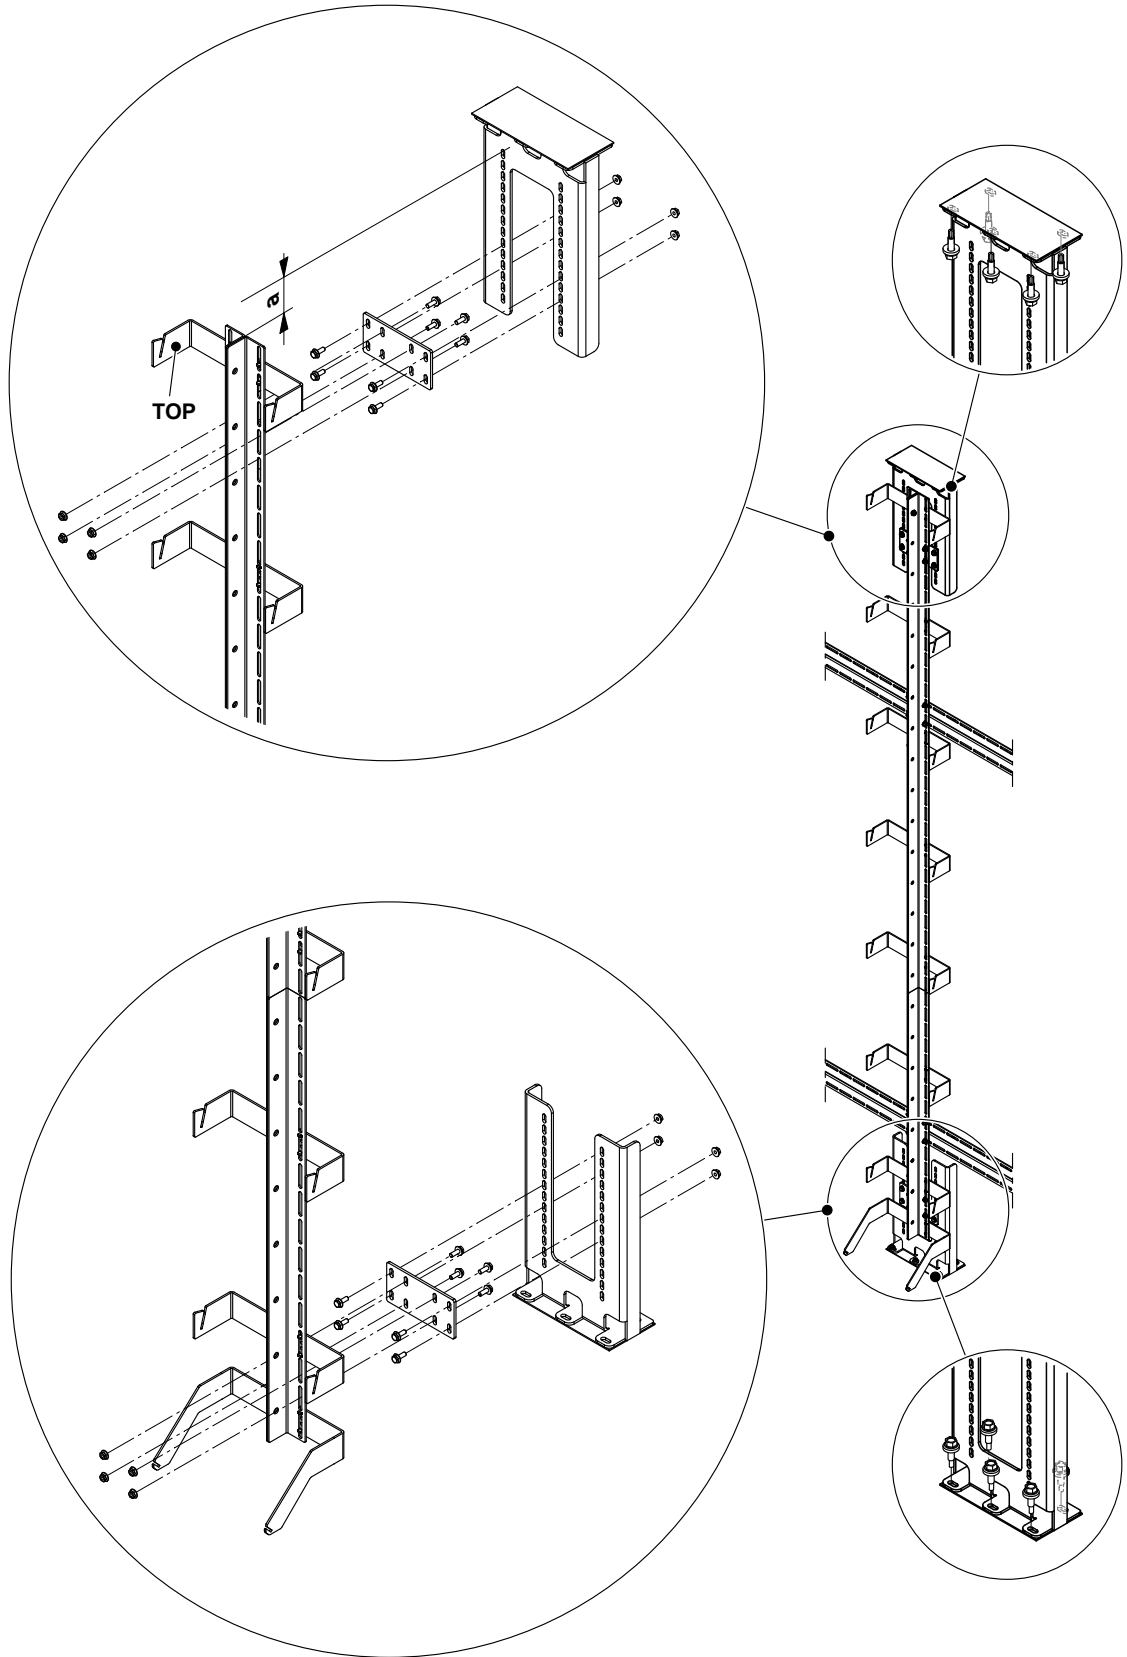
Montaje de lo(s) apoyo(s) vertical(es) con pata de apoyo superior e inferior:
